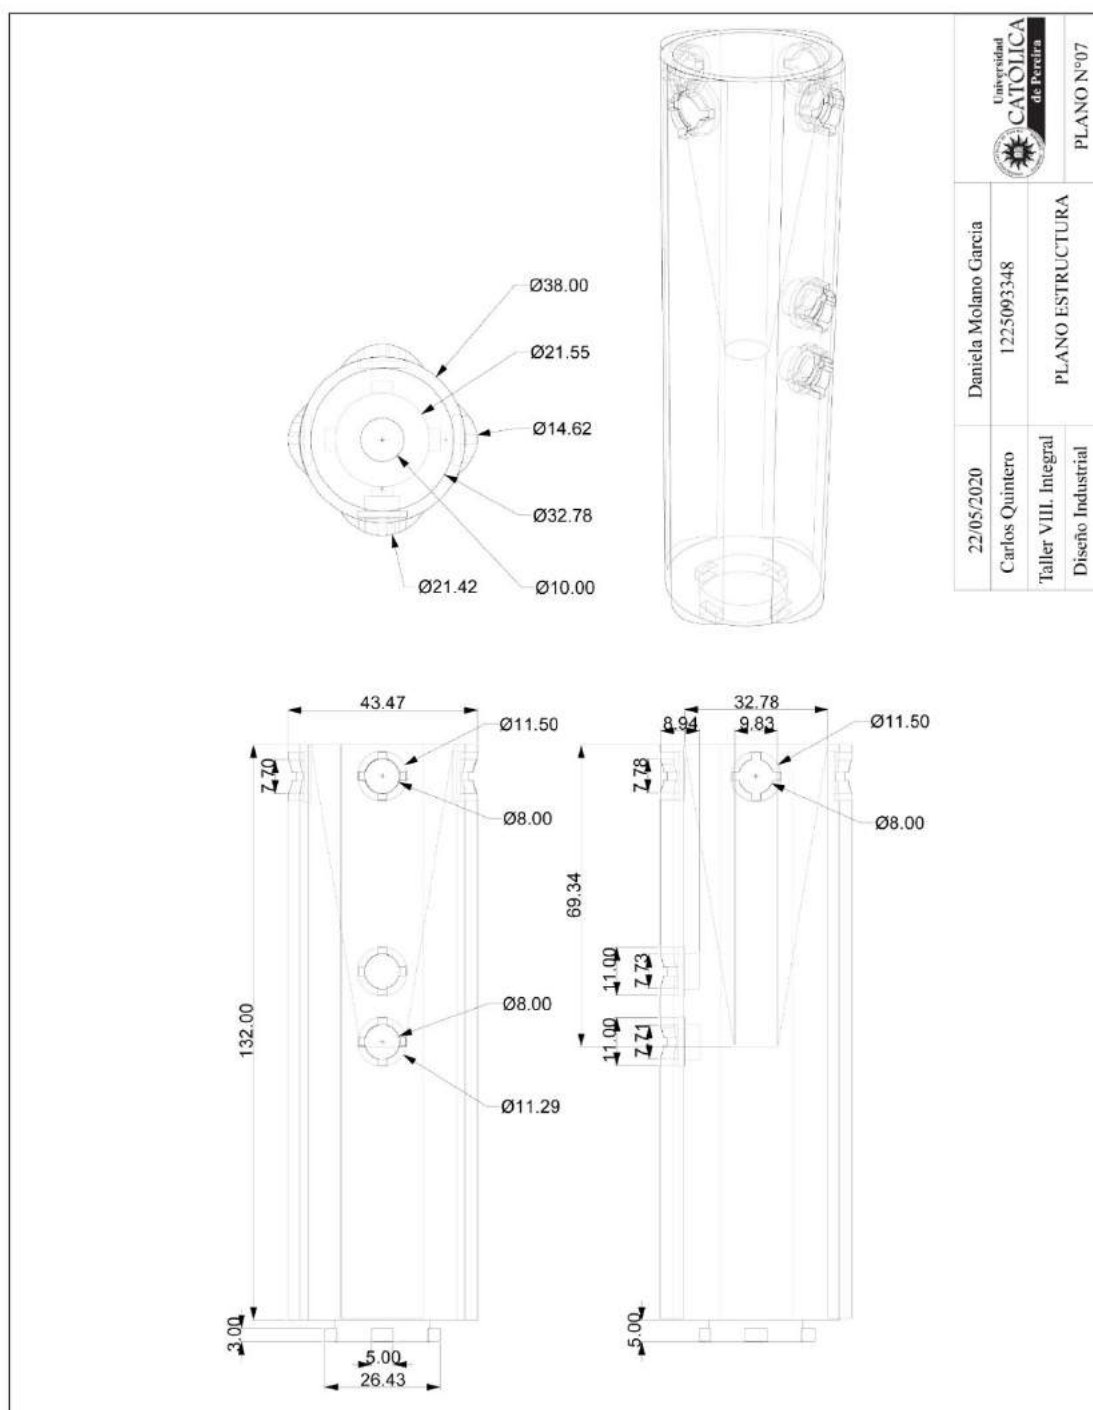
Planos técnicos, explosión. Fuente: Elaboración propia.
